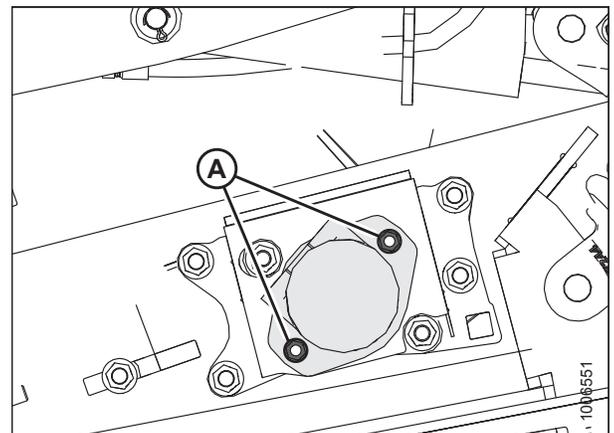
Motor hidráulico delantero; lado izquierdo
